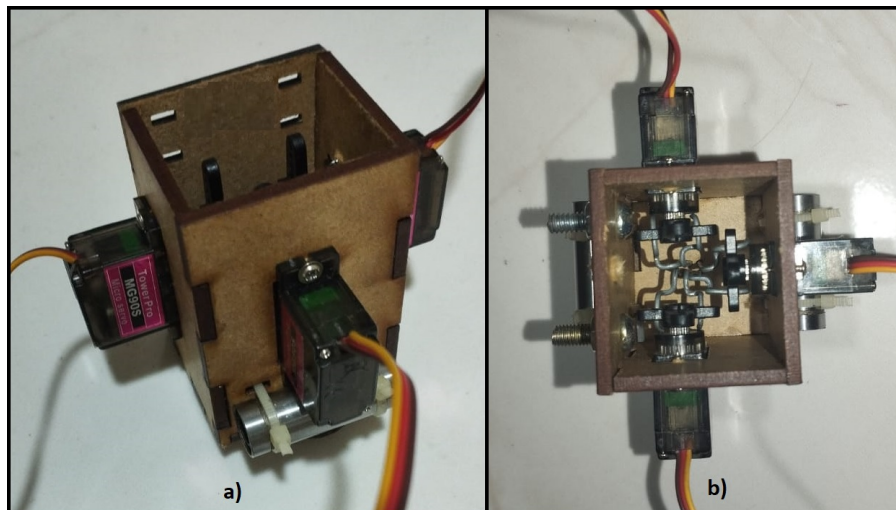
Cabeça de Impressão desenvolvida com peças estruturais em MDF cortado a laser - a) ênfase parte externa; b) ênfase parte interna.
